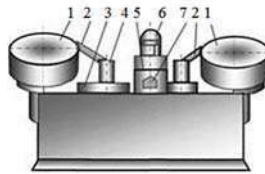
Схема компоновки однопозиционного сборочного автомата
